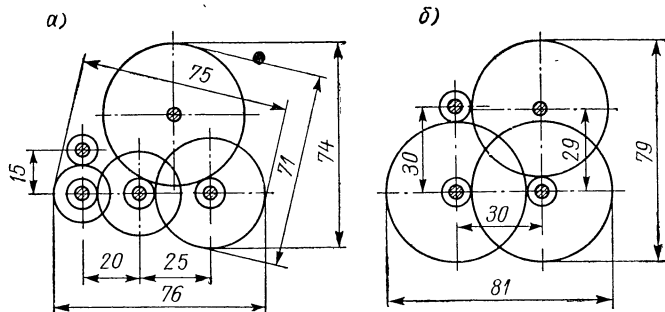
Компоновочные эскизы: а — четырехступенчатого редуктора; б — трехступенчатого редуктора
